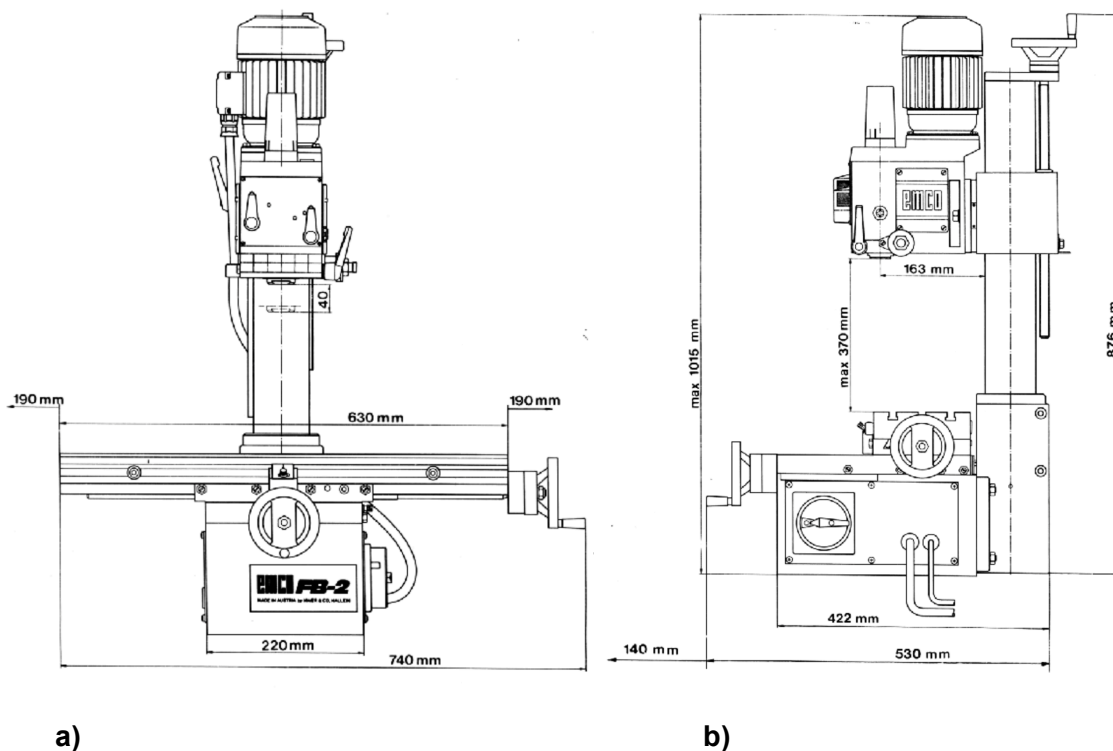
a,b: Koordinaten Fräs- und Bohrmaschine des Typs FB-2 der Firma EMCO in Frontalansicht (a) und Seitansicht (b). Der Motor der Fräse ist über dem Werkstück fest montiert. Das Bearbeiten des Werkstoffes wird durch die Bewegungen des Werkstückes über die Einstellräder gesteuert. Die Bewegungen des Werkstückes lassen sich in allen 3 Raumebenen Stufenlos einstellen.
